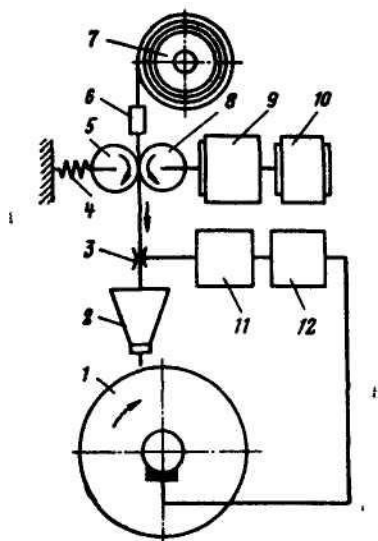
Схема установки для автоматичного наплавлення під шаром флюсу
